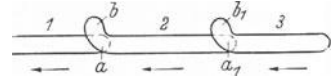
Nahtschritte beim Aluminiumschweißen.
